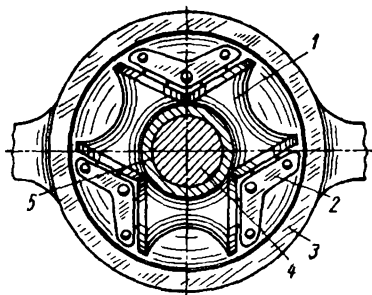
Роликовая матрица для протяжки: 1 — ролик; 2 — кронштейны; 3 — корпус; 4 — протяжной пуансон; 5 — протягиваемая поковка
